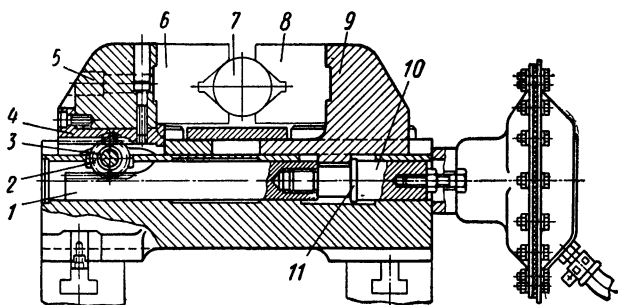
Призматический механизм с реечно-зубчатым приводом к ползунам
